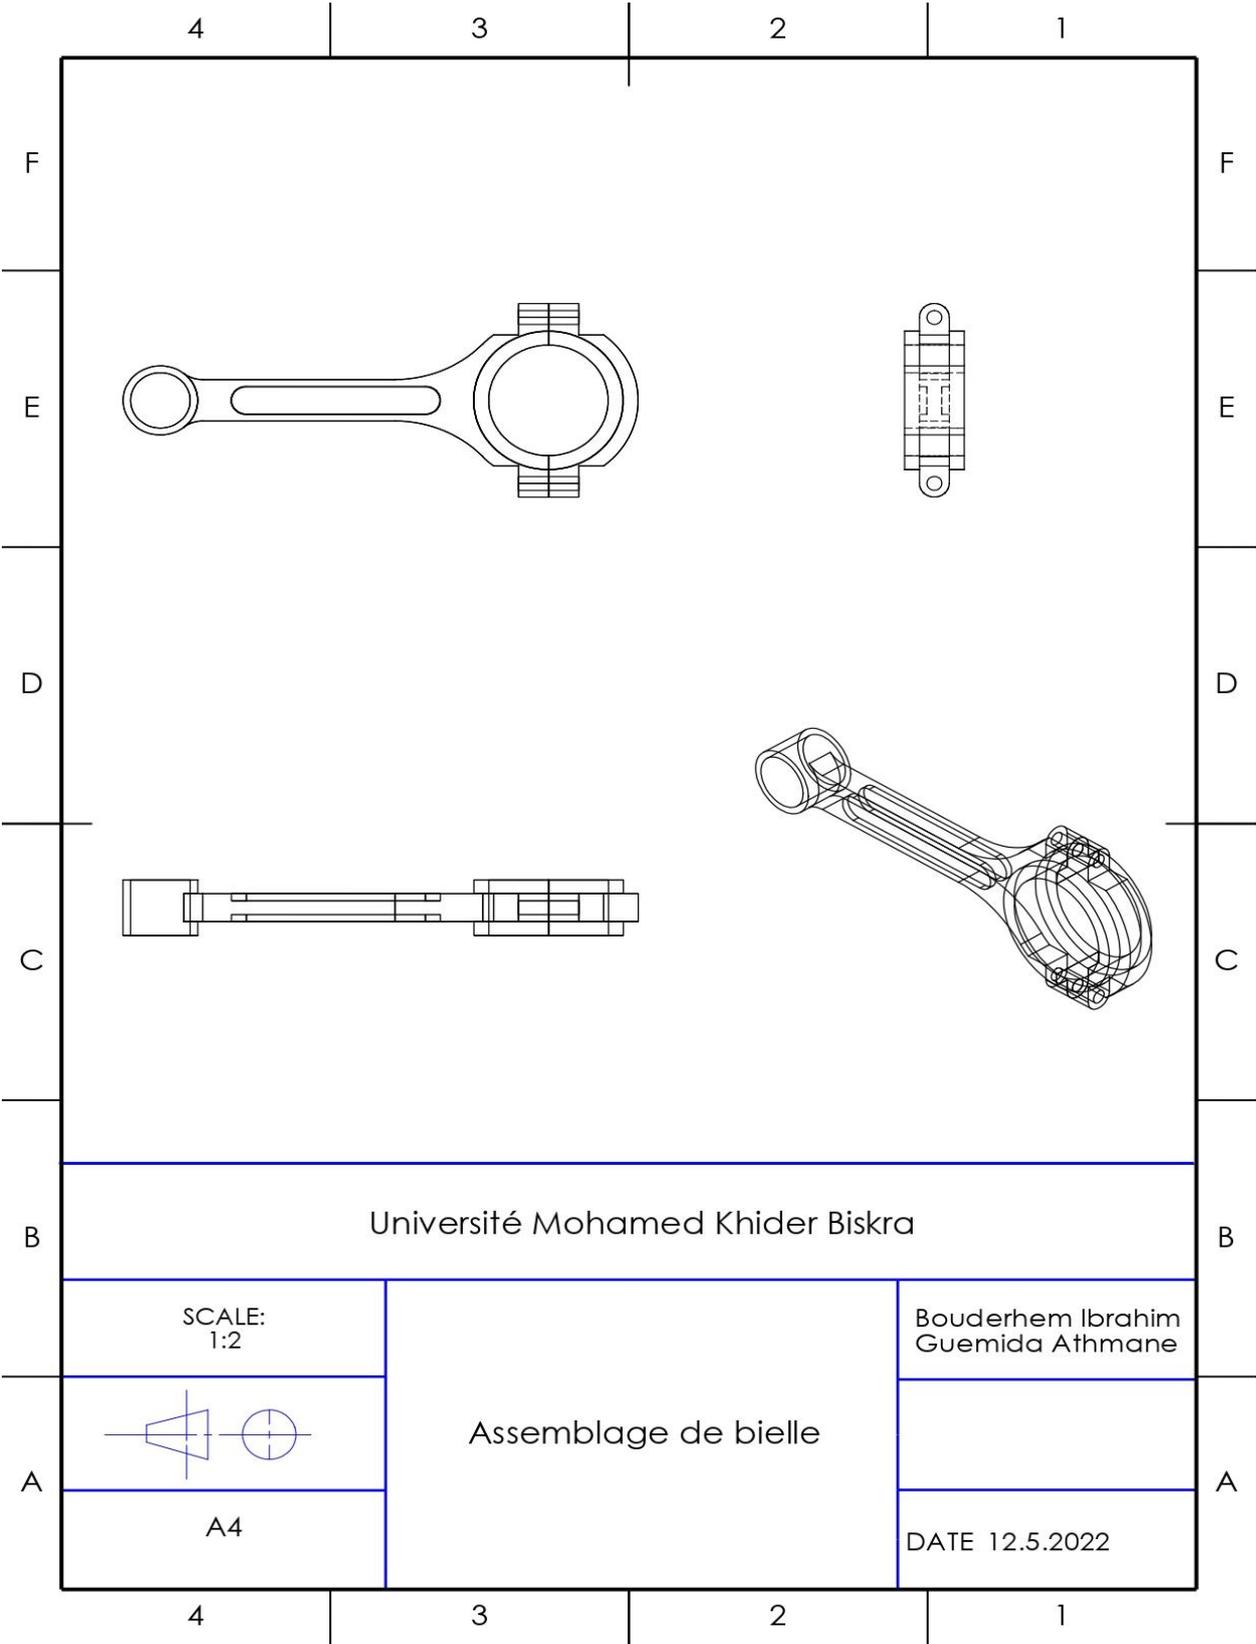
Dessin définition d'un assemblage corps et chapeau de la bielle.
